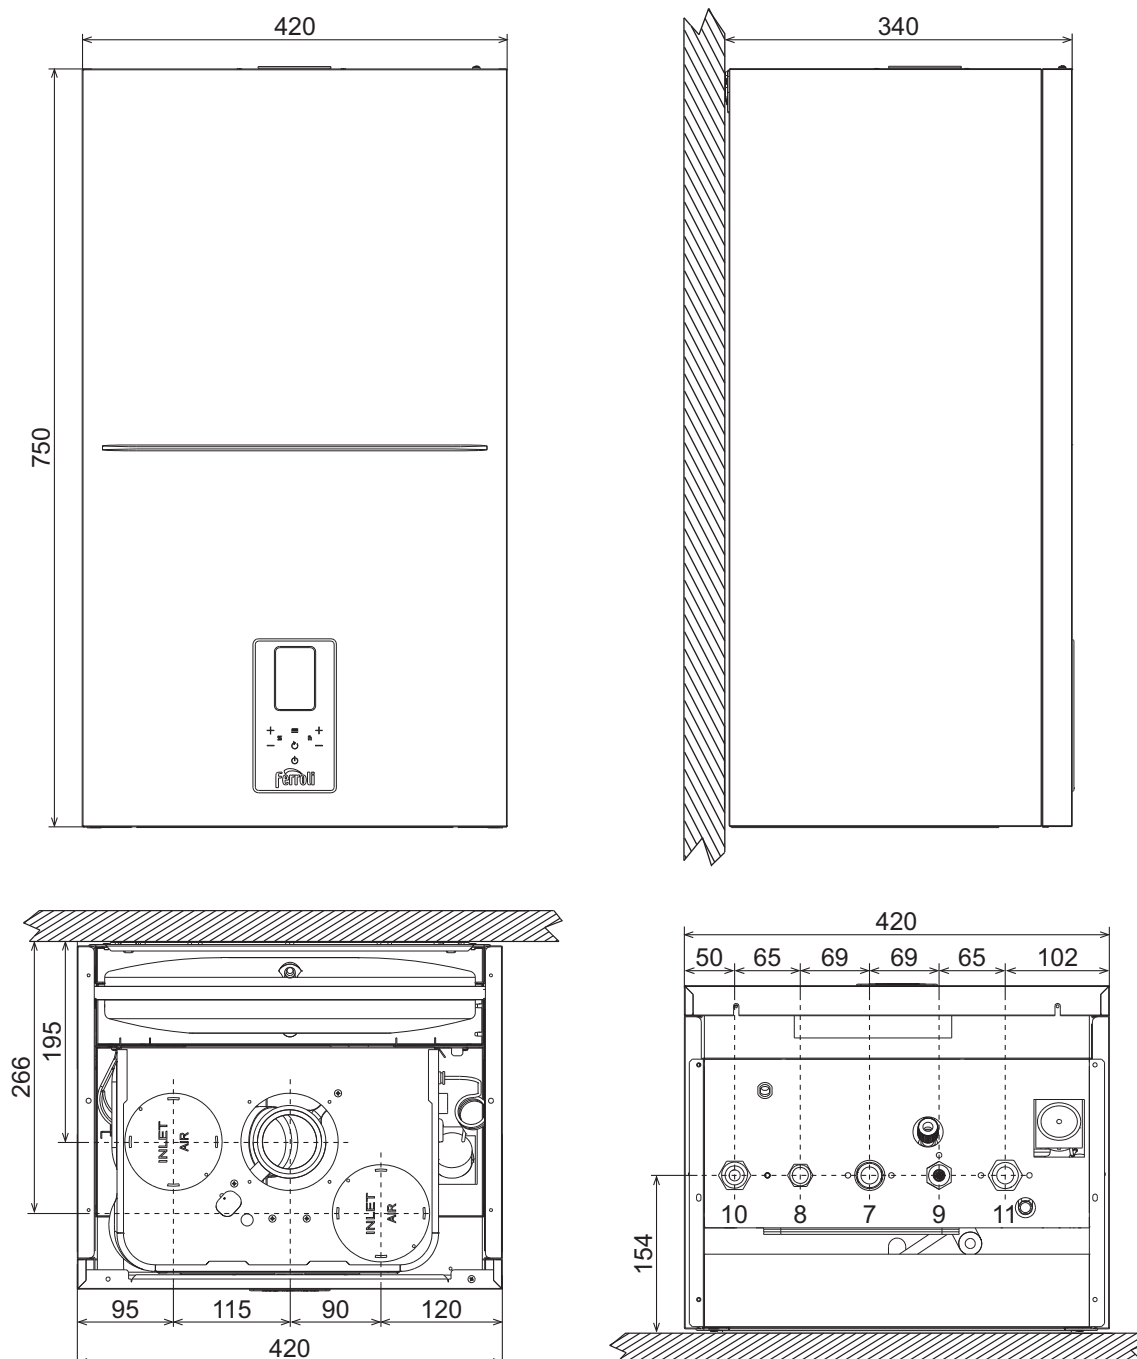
Dimensions et raccords modèle DIVATOP D F24
